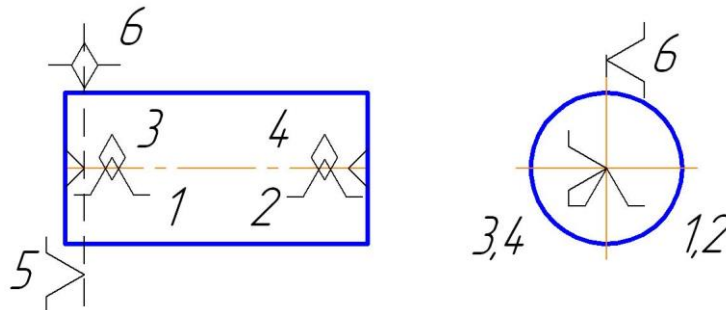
Теоретична схема базування при обробці на токарних верстатах
